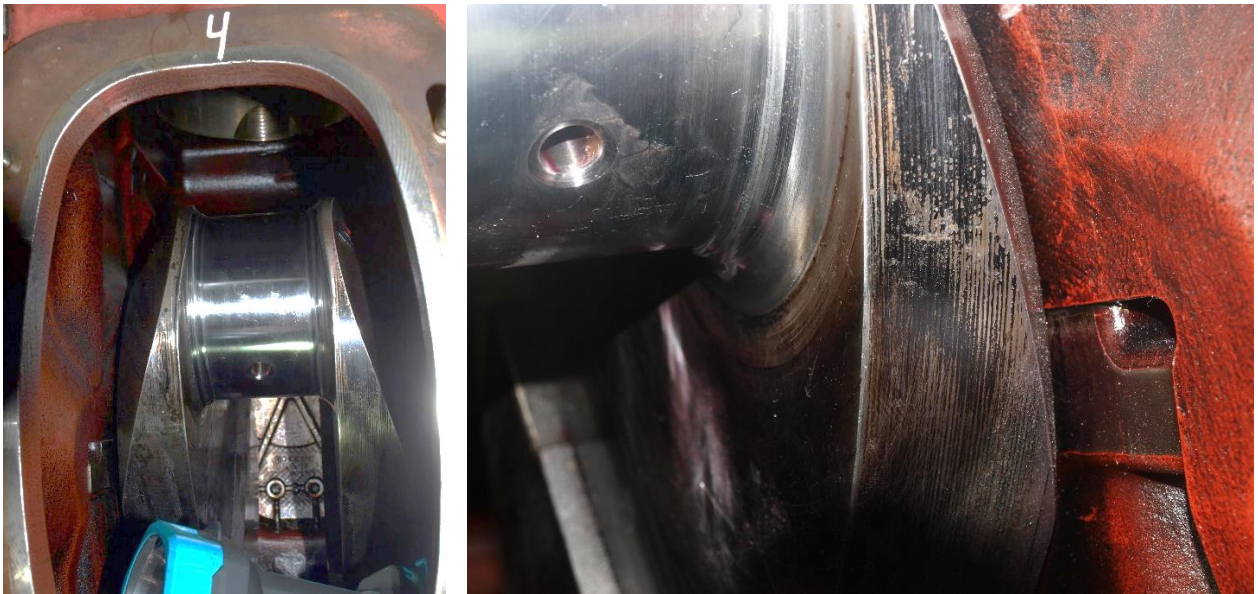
Мотылёвая шейка коленчатого вала двигателя МАК модели 6М20 (6ЧН20/30) после проточки и чистовой обработки
